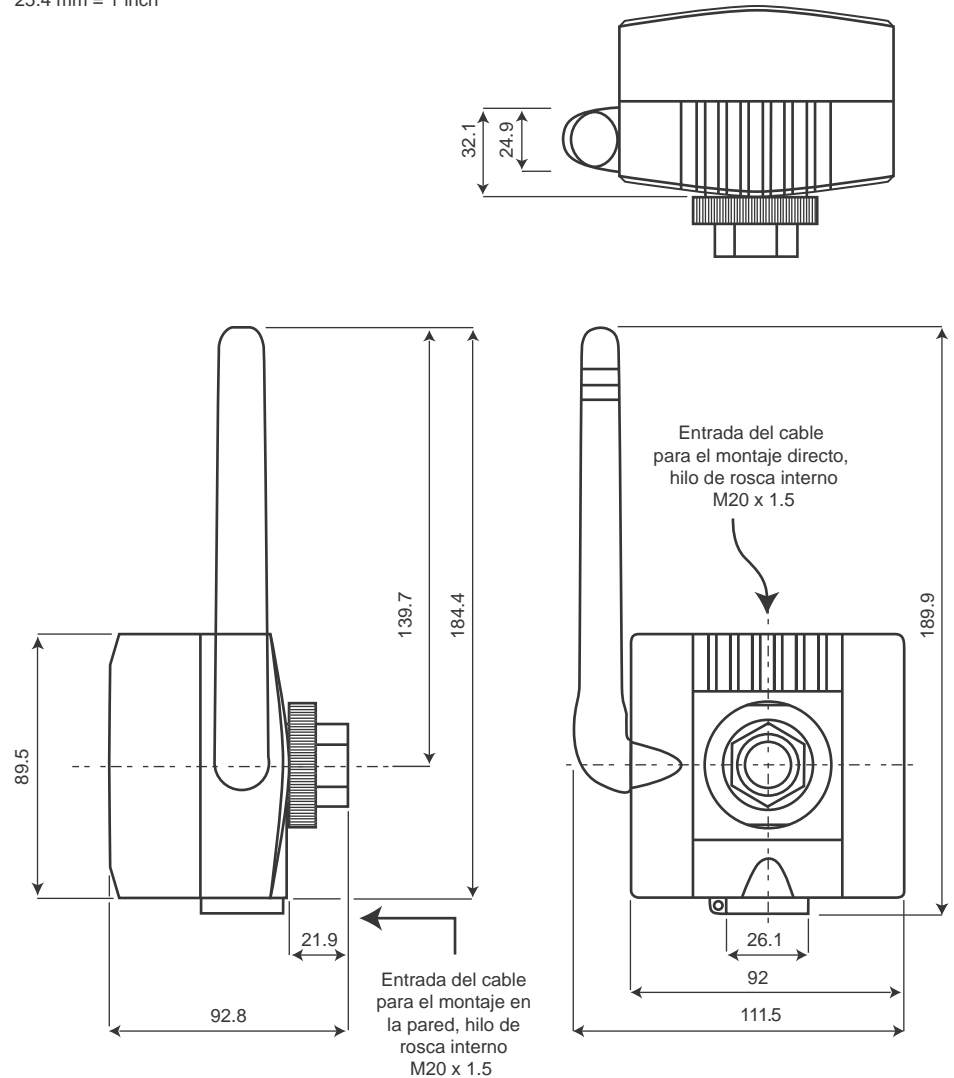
Dimensiones del adaptador inalámbrico SWA70
